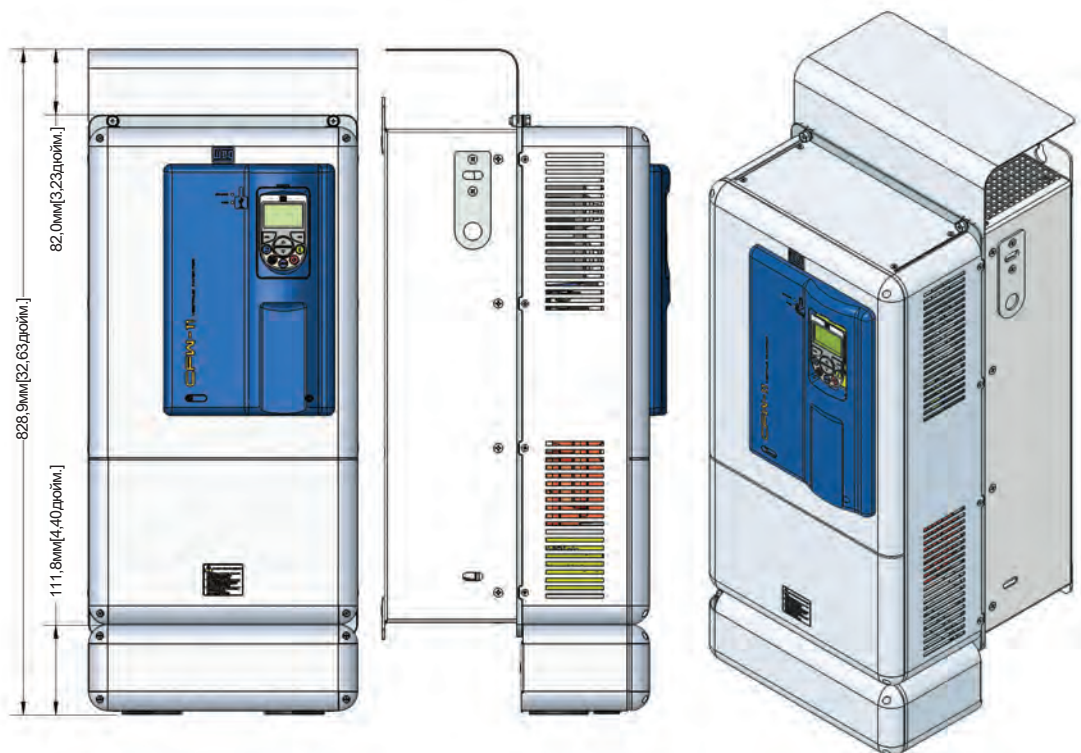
Габаритные размеры преобразователя, модель с дополнительной степень защиты IP55, размер корпуса E, мм [дюйм.]
